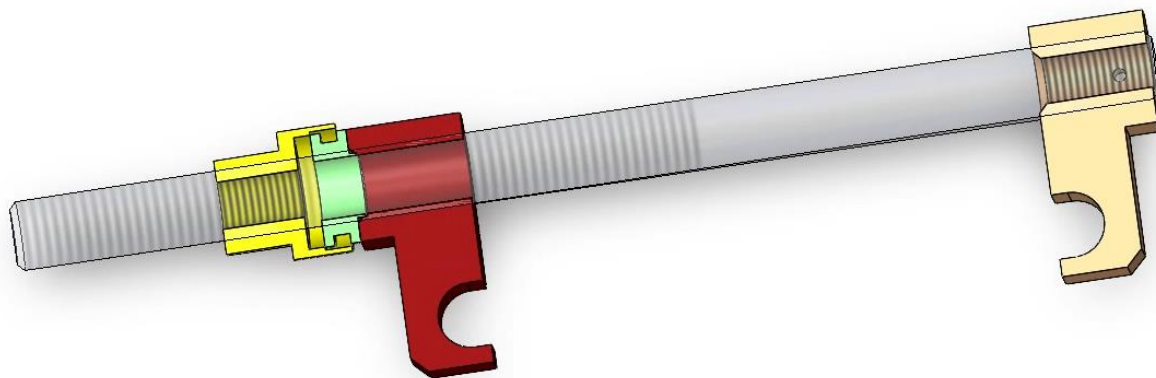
Вид стяжки в разрезе по оси стержня
